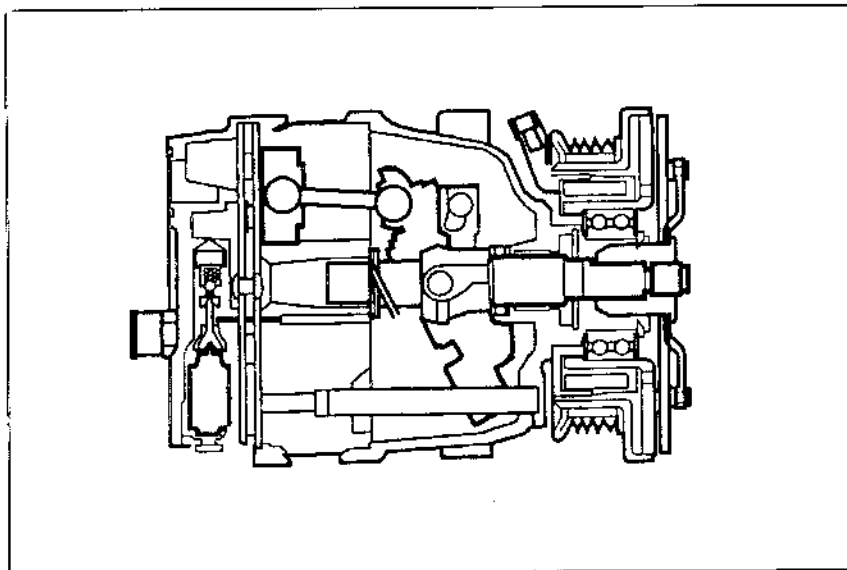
Вид аксиально-поршневого компрессора в разрезе.
